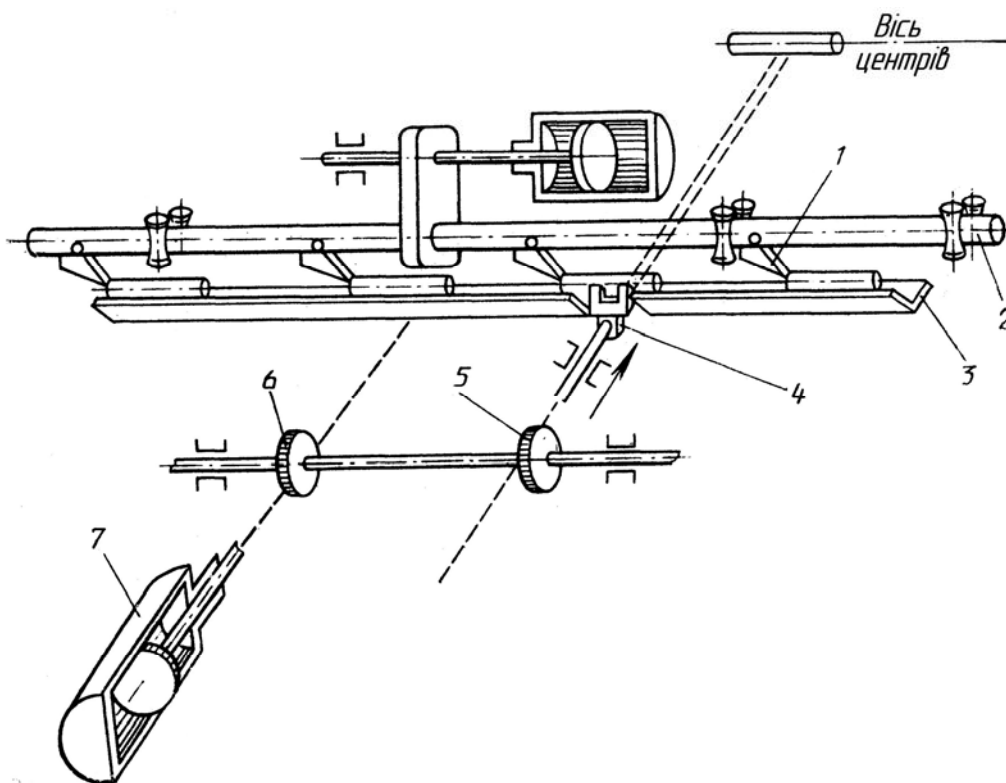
Конструктивна схему транспортної системи з автооператором для обробки заготовок типу валів електродвигунів
